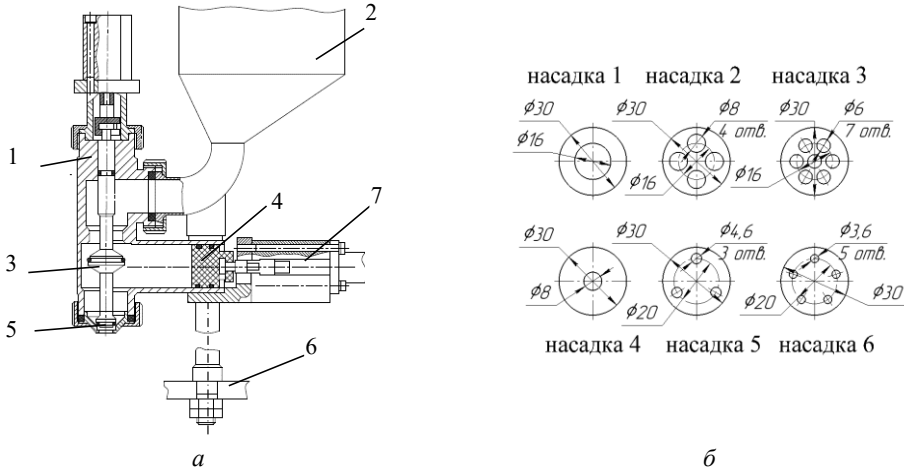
Пневматичний поршневий дозувальний модуль: а — схема дозувального модуля; б — схема насадки: 1 — корпус; 2 — бункер; 3 — клапан; 4 — поршень; 5 — насадка; 6 — кріплення; 7 — пневмоциліндр
